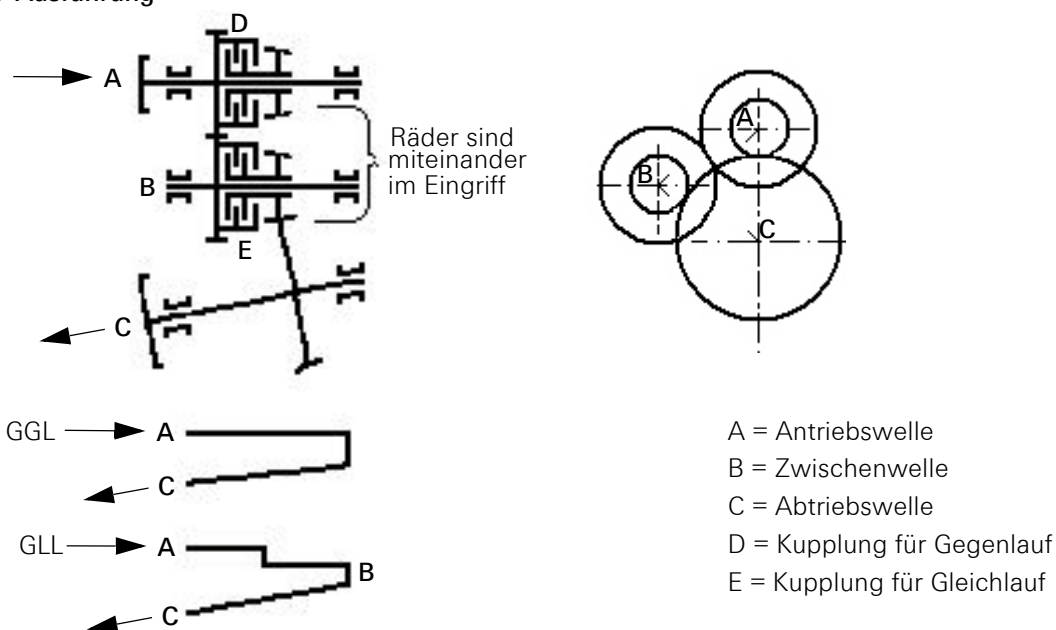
Kraftflussschema der V-Ausführung (Beispiel, GLL = Gleichlauf, GGL = Gegenlauf)
